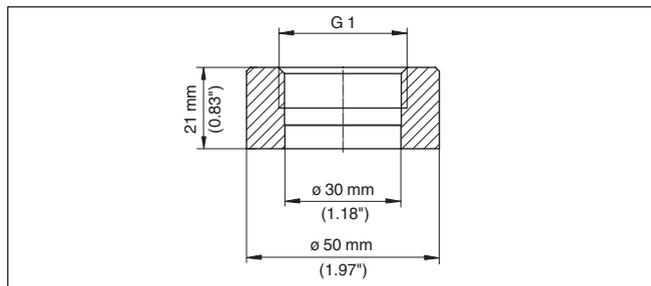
Dimensions raccord à souder G1 (ISO 228-1) - VEGABAR 82, 83
